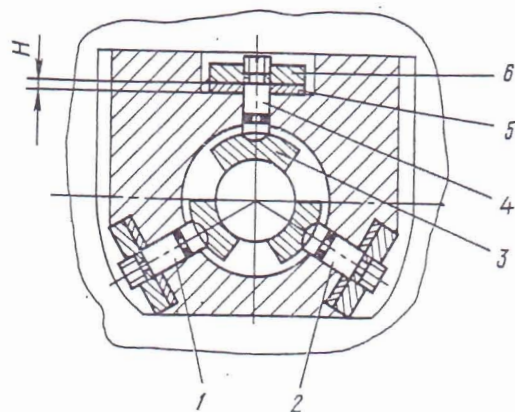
Регулирование зазоров в подшипниках шпинделя (передняя опора) для станков ЗЕ711ВФ1, ЗЕ711АФ1, ЗЕ721АФ1-1
